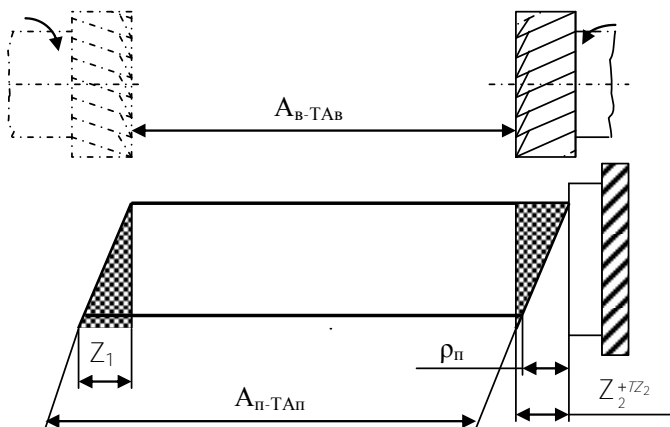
Схема двусторонней обработки с базированием по обрабатываемой поверхности
